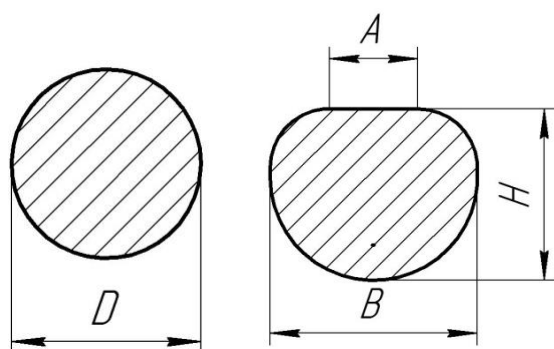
Форма и основные размеры поперечного сечения заготовки до и после двухопорной пластической гибки
